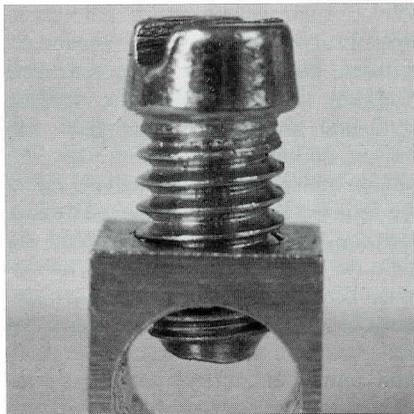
Klemmstelle einer Einzelverbindungsklemme
